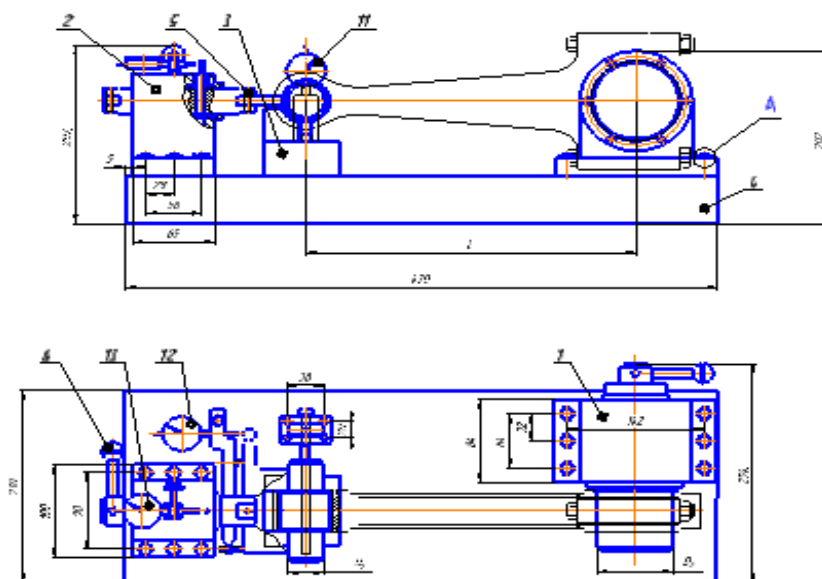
Конструкция разработанного устройства для проверки шатунов
